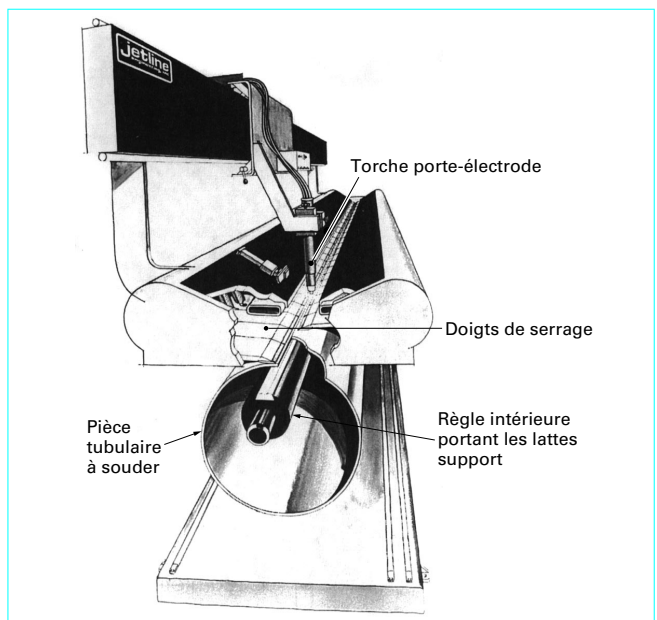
Banc de soudage de tubes de faible épaisseur
